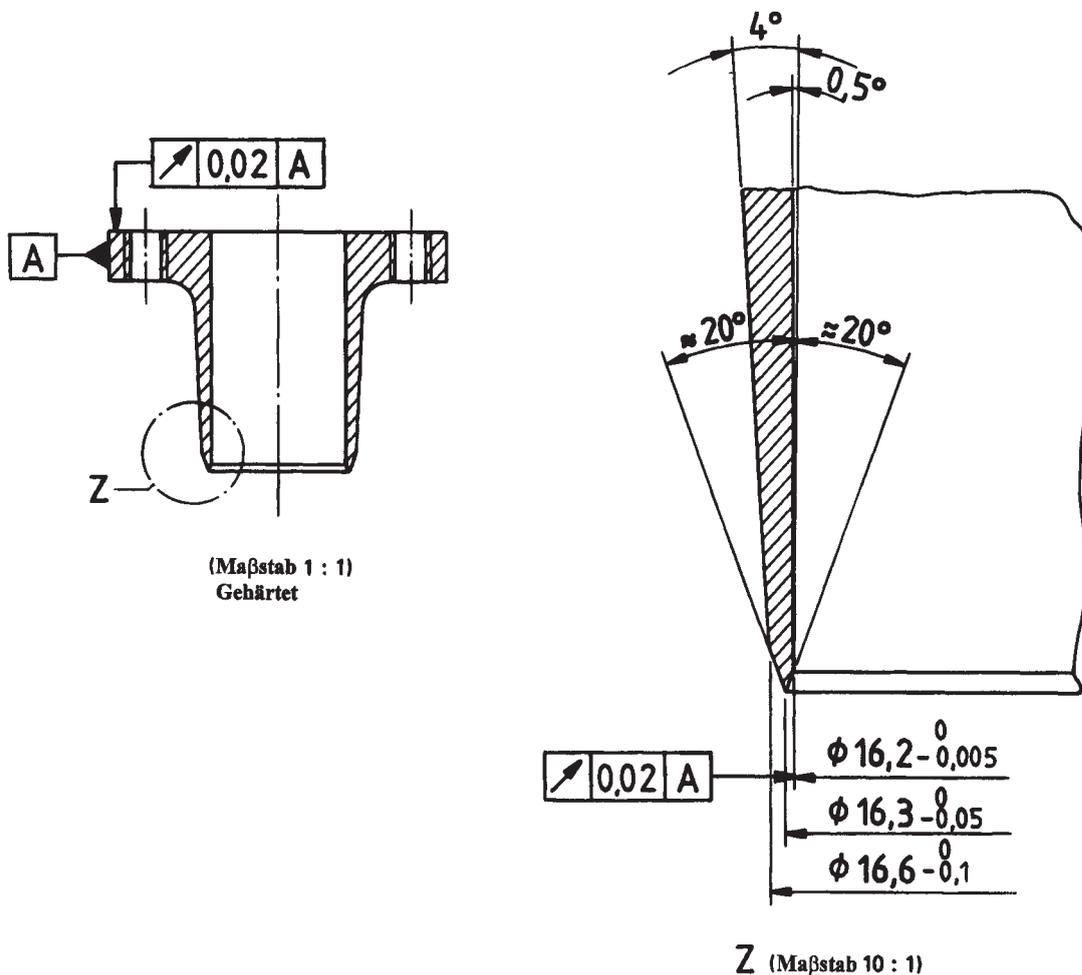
Hohlbohrer für die Vorbereitung des Prüfstücks
